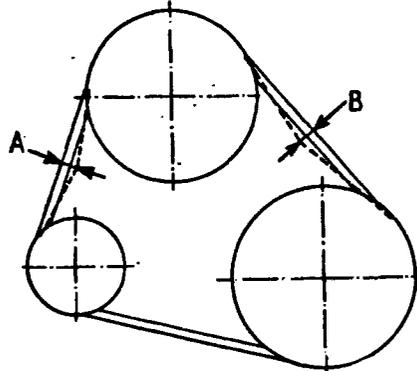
Схема проверки натяжения ремня привода насоса
